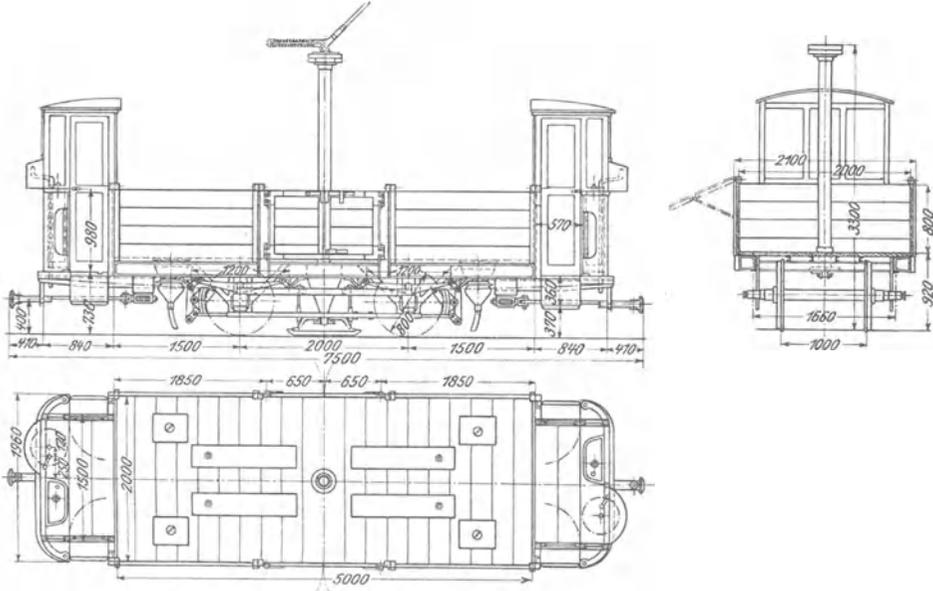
Offener Güterwagen (Triebwagen) der Stuttgarter Straßenbahn.
